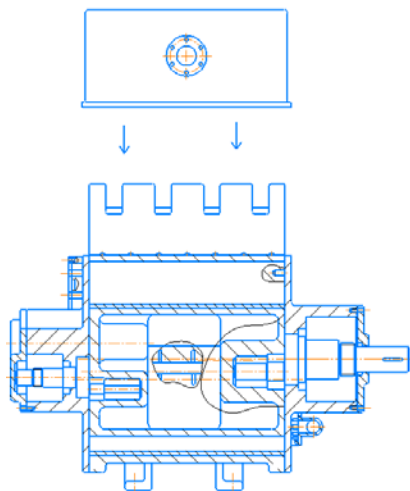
Схема присоединения верхней крышки с механизмом прижима пластин к корпусу комбинированного насоса
